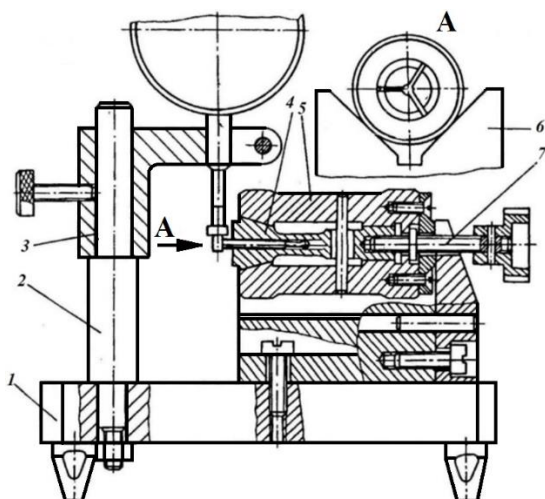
Приспособление для контроля биения ступенчатого валика
